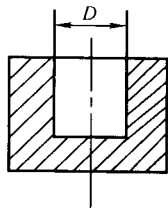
工件预加工尺寸和螺纹尺寸关系
